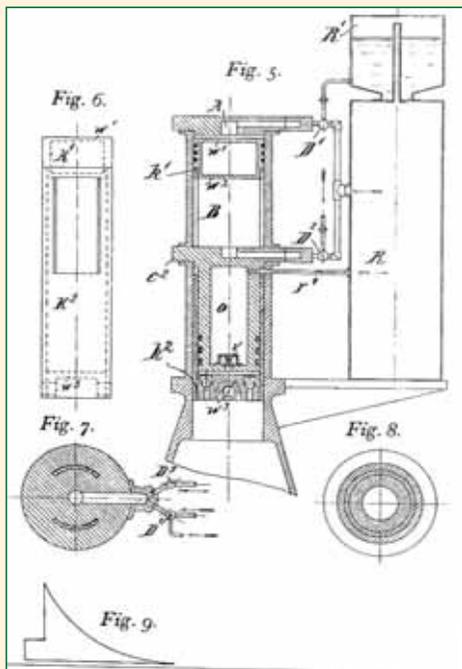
Второй вариант "батарейного" двигателя Б. Г. Луцкого: А и В - камеры сжатия; К1 и К2 - поршни, жестко соединенные между собой; С2 - крышка; D1, D2, и D3 - поворотные золотники; w1 и w2 днища поршня К1; w3 - днища поршня К2; v - клапан; R - сосуд; R1 - дополнительный сосуд
